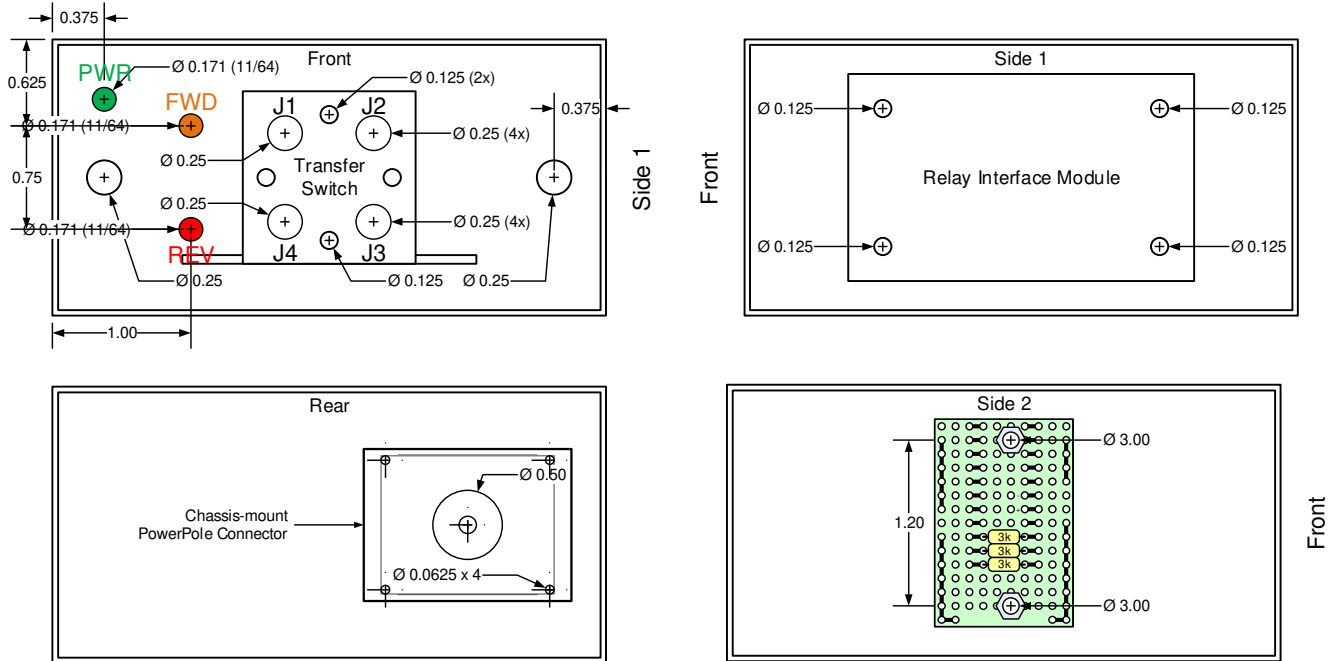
~ Die Layoutzeichnung des Gehäuses zeigt die Schnitt- und Bohrabmessungen. Alle Maße sind in Zoll angegeben, sofern nicht anders angegeben. Die Montageabmessungen des Übertragungsschalters hängen vom tatsächlich verwendeten Schalter ab. Wie im Text erwähnt, kann die PWR-LED entfernt werden.
